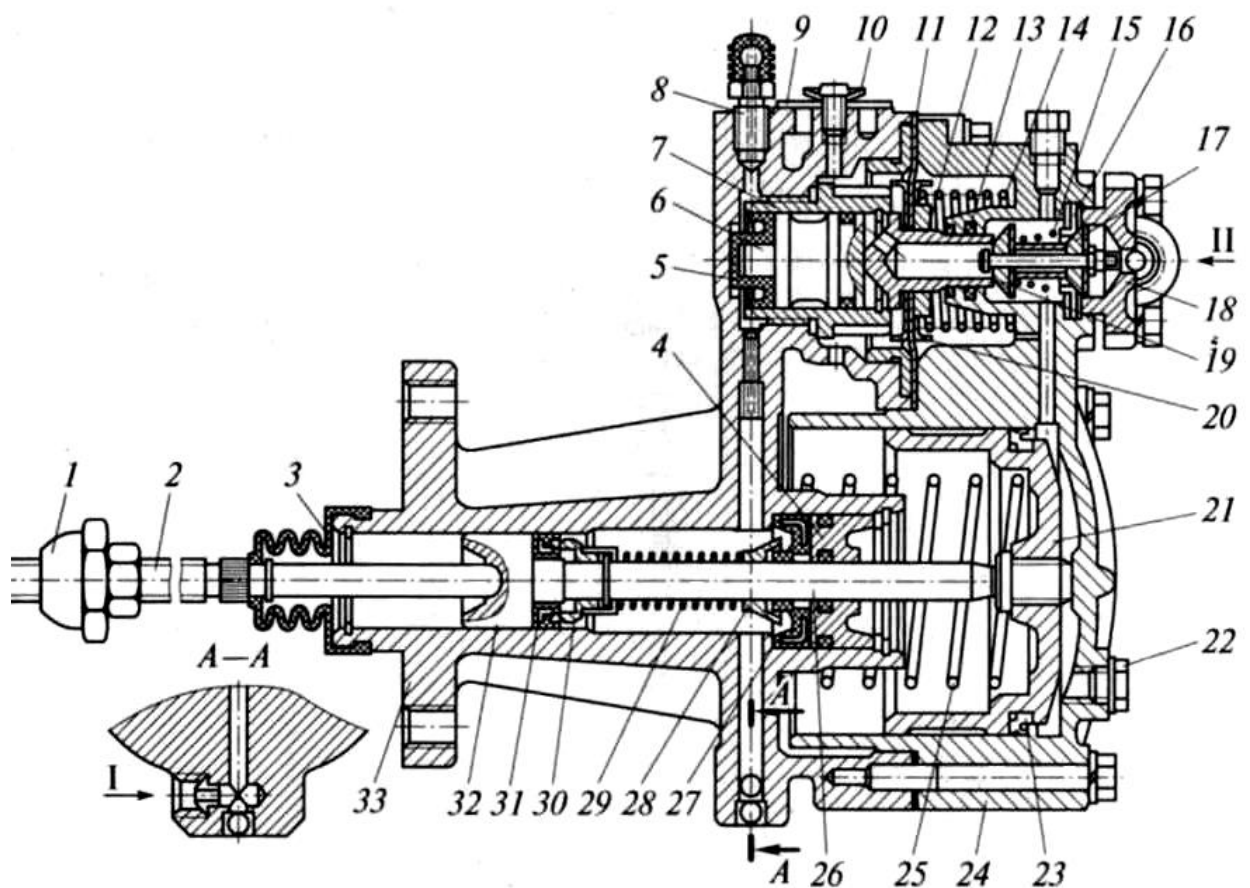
Пневмогидравлический усилитель привода сцепления автомобилей КАМАЗ:
